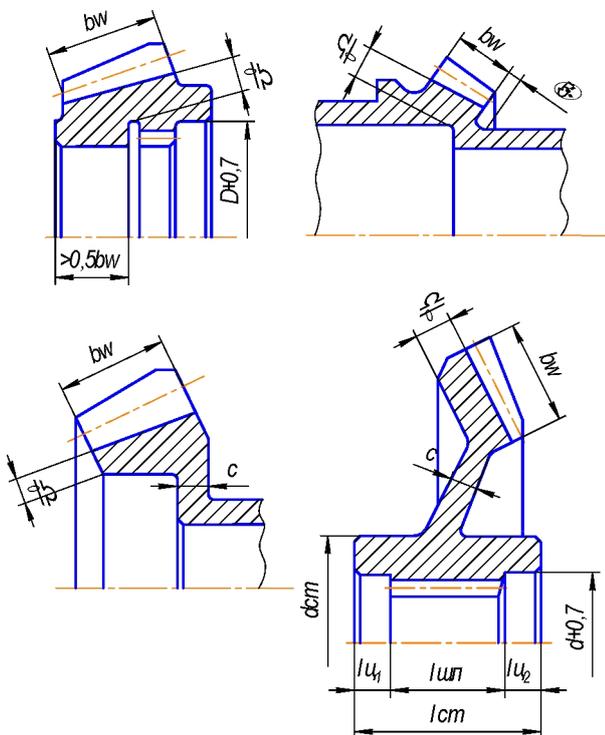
Варианты конструкции и параметры конических зубчатых колёс внешнего зацепления
